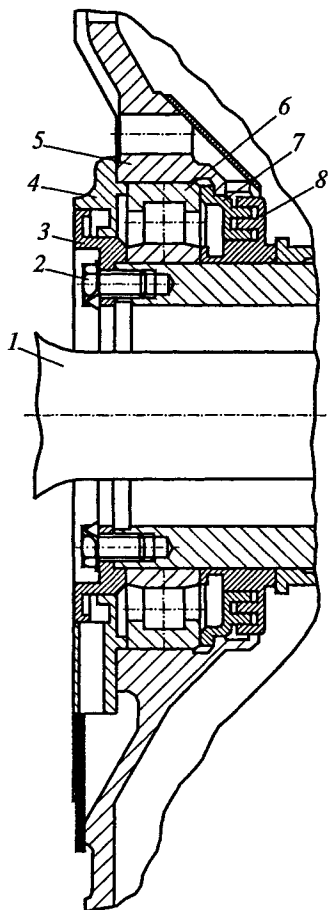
Малый подшипниковый щит электродвигателя НБ-520В:
